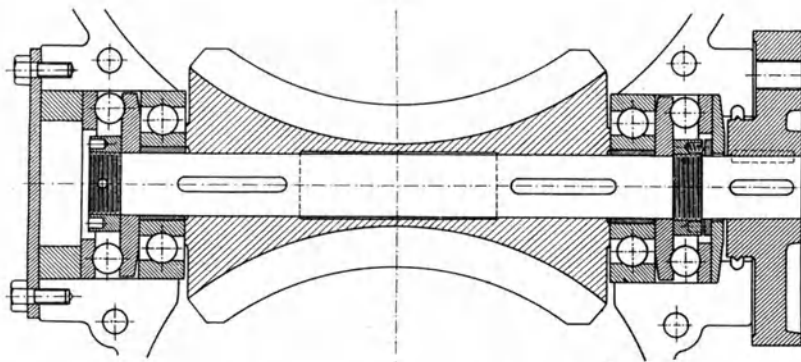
Ausführung der Maschinenfabrik Pekrun, Coswig.
